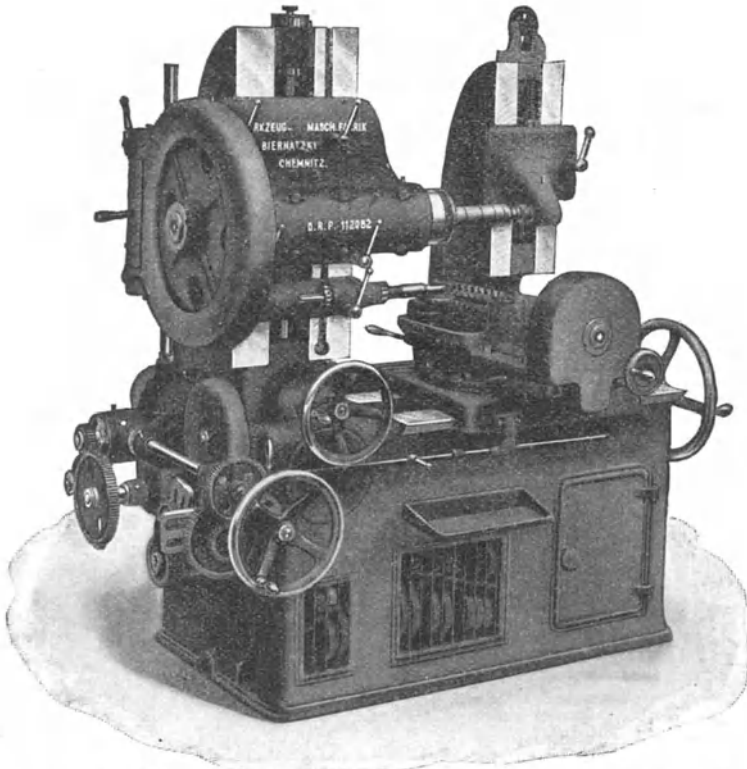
Räderfräsmaschine nach dem Abwälzverfahren von Biernatzki & Co.
